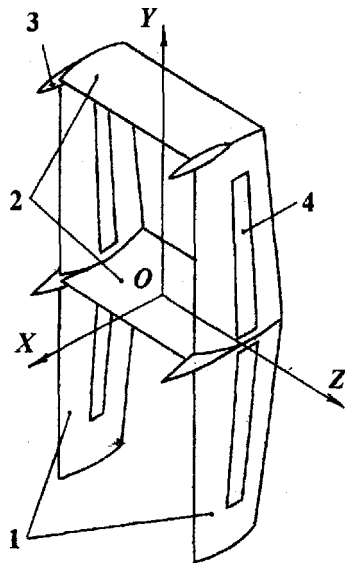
Загальний вигляд тягового біпланового модуля вітроколеса:
